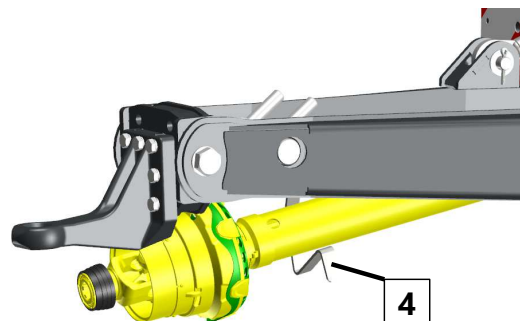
Держатель карданного вала в позиции верхней сцепки
